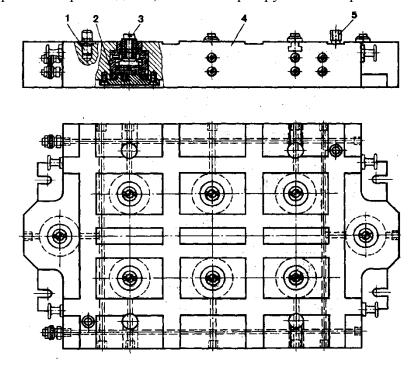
Гидравлический стол — базовая часть приспособления гидравлического универсально-наладочного
